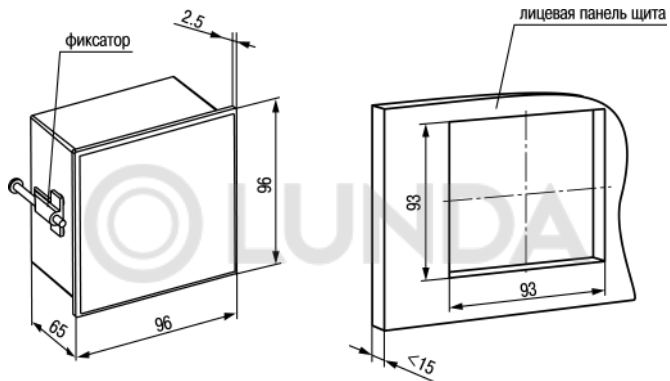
Габаритные размеры корпуса Щ1
